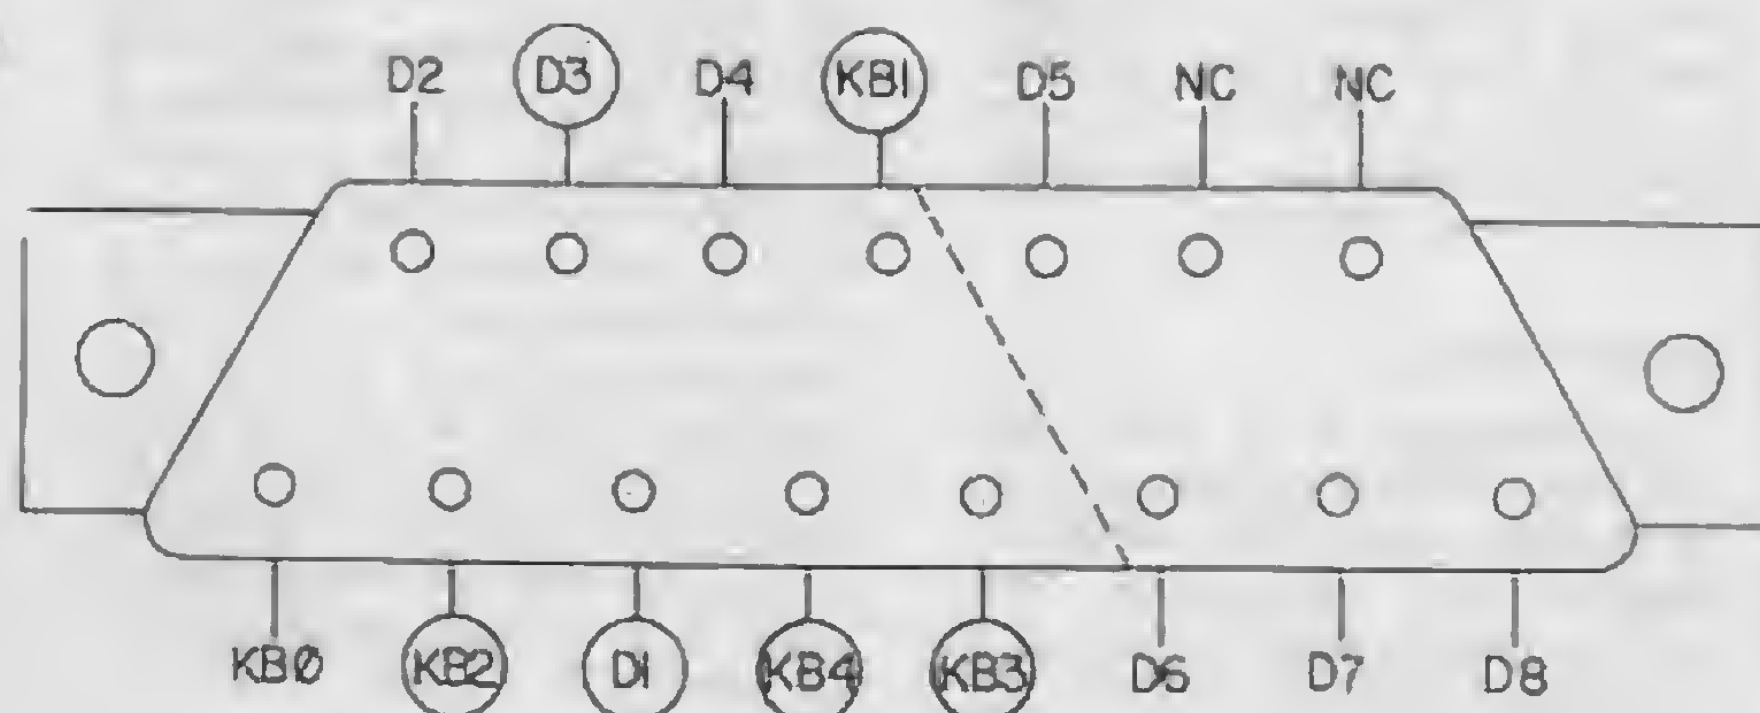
Vista de la plaqueta en su cara de soldaduras, mostrando los puntos a soldar.
